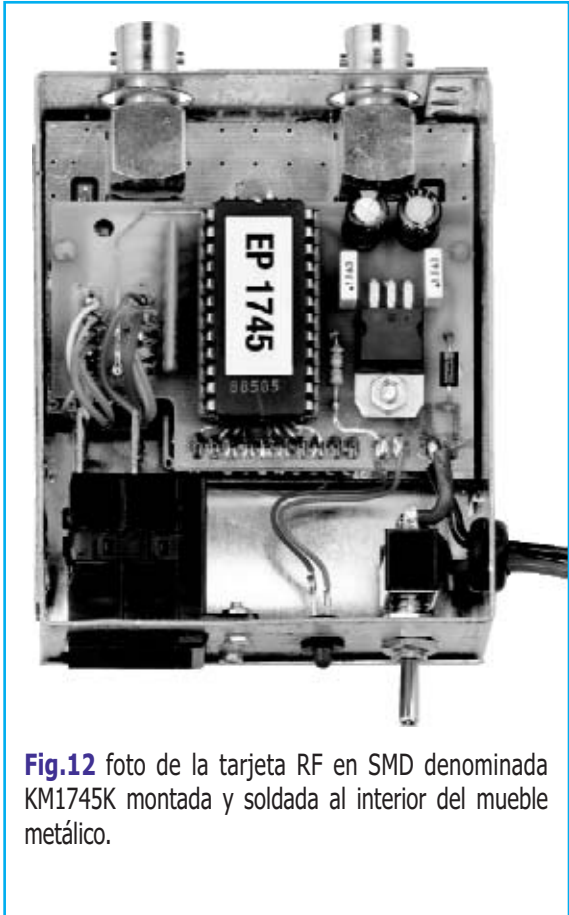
foto de la tarjeta RF en SMD denominada KM1745K montada y soldada al interior del mueble metálico.
